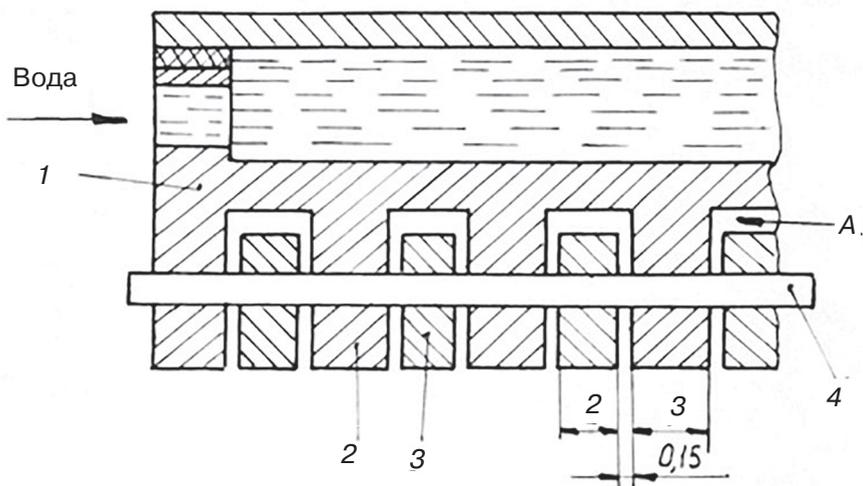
Схема верхньої стінки форми: 1 – корпус; 2 – гребінка; 3 – вставні пластини; 4 – фіксатор; А – зазор 2–3 мм
